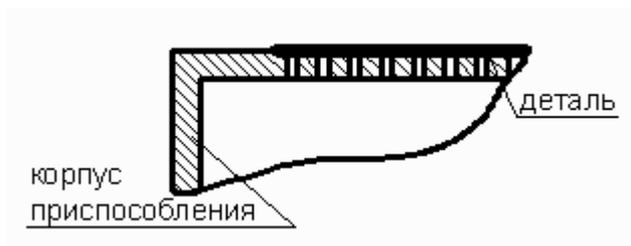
Схема закрепления легко деформируемых заготовок.
